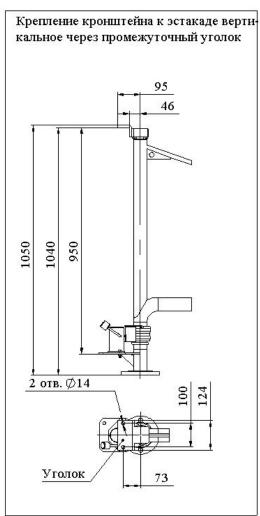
Установочные размеры стояка слива-налива жидкой фазы.
